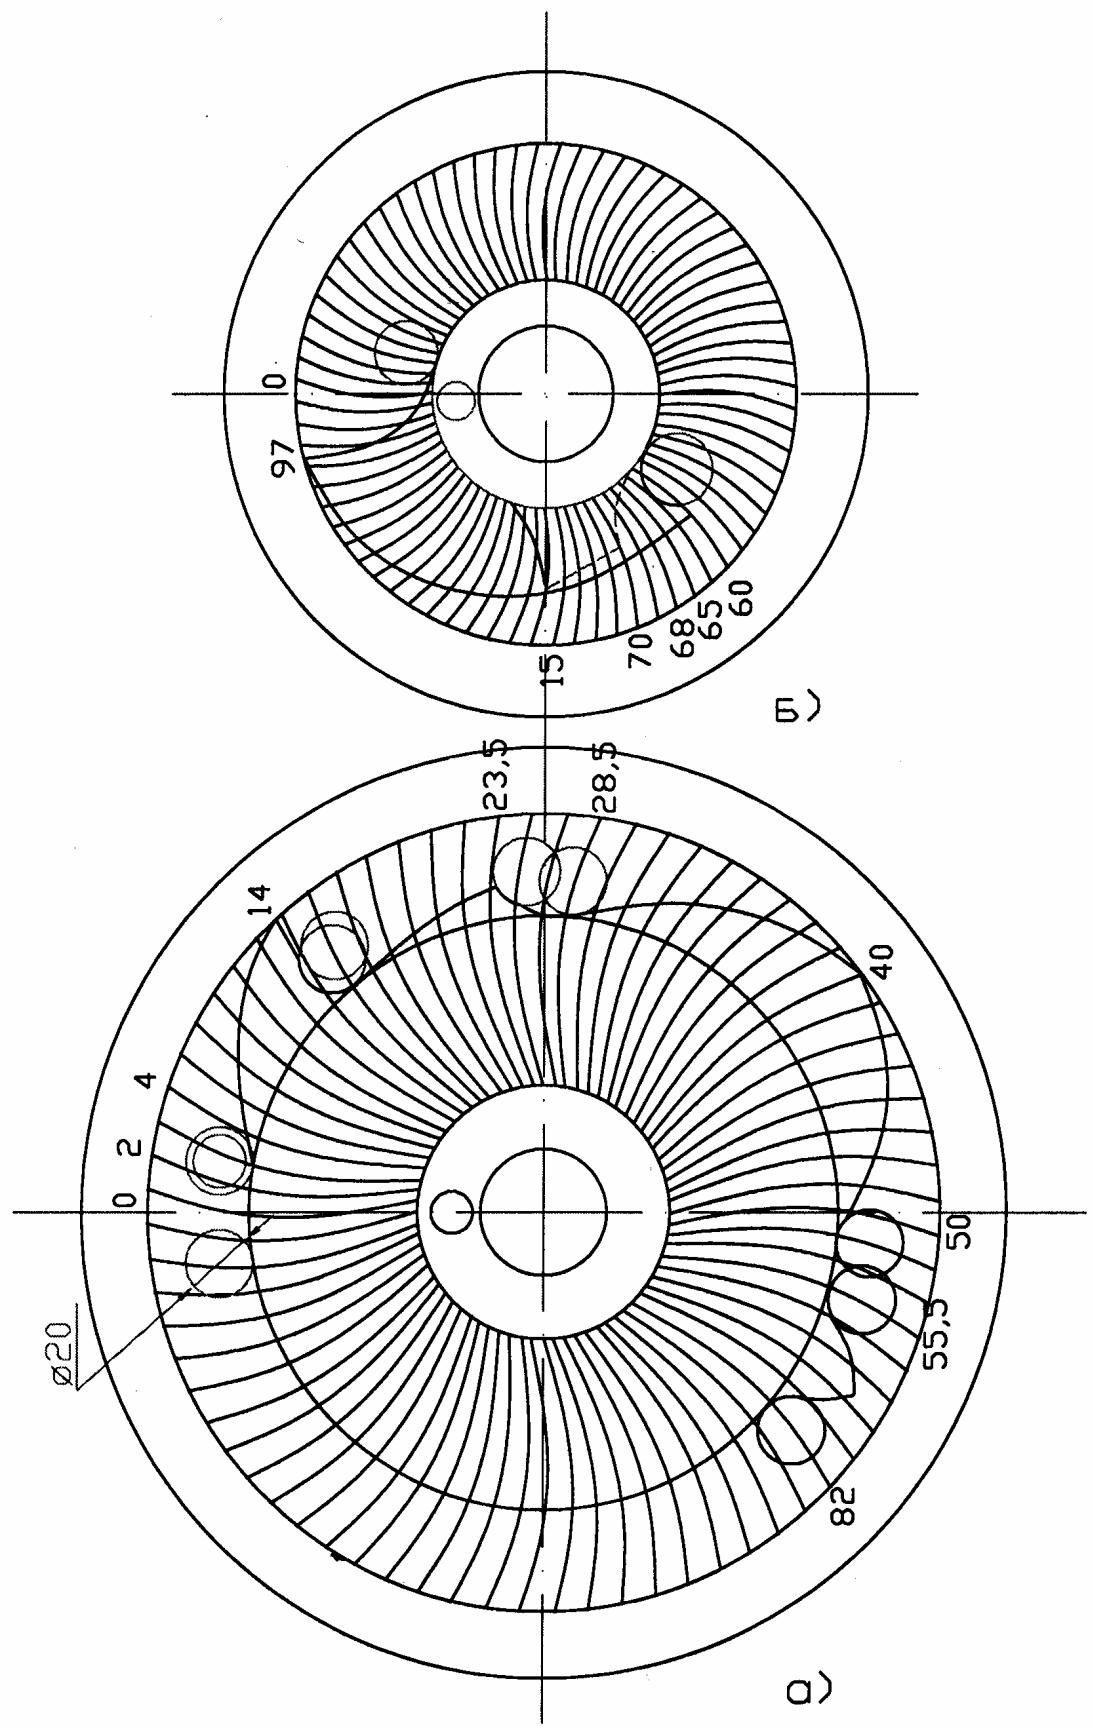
Рабочий профиль кулачка: а – револьверного суппорта; б – поперечного суппорта
